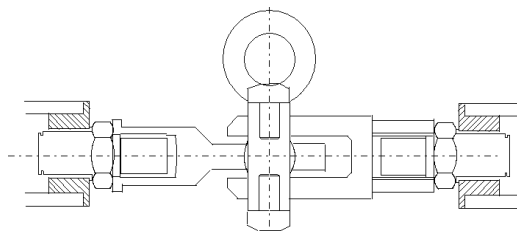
Dispositif de Connexion des Barres[NGU09]
